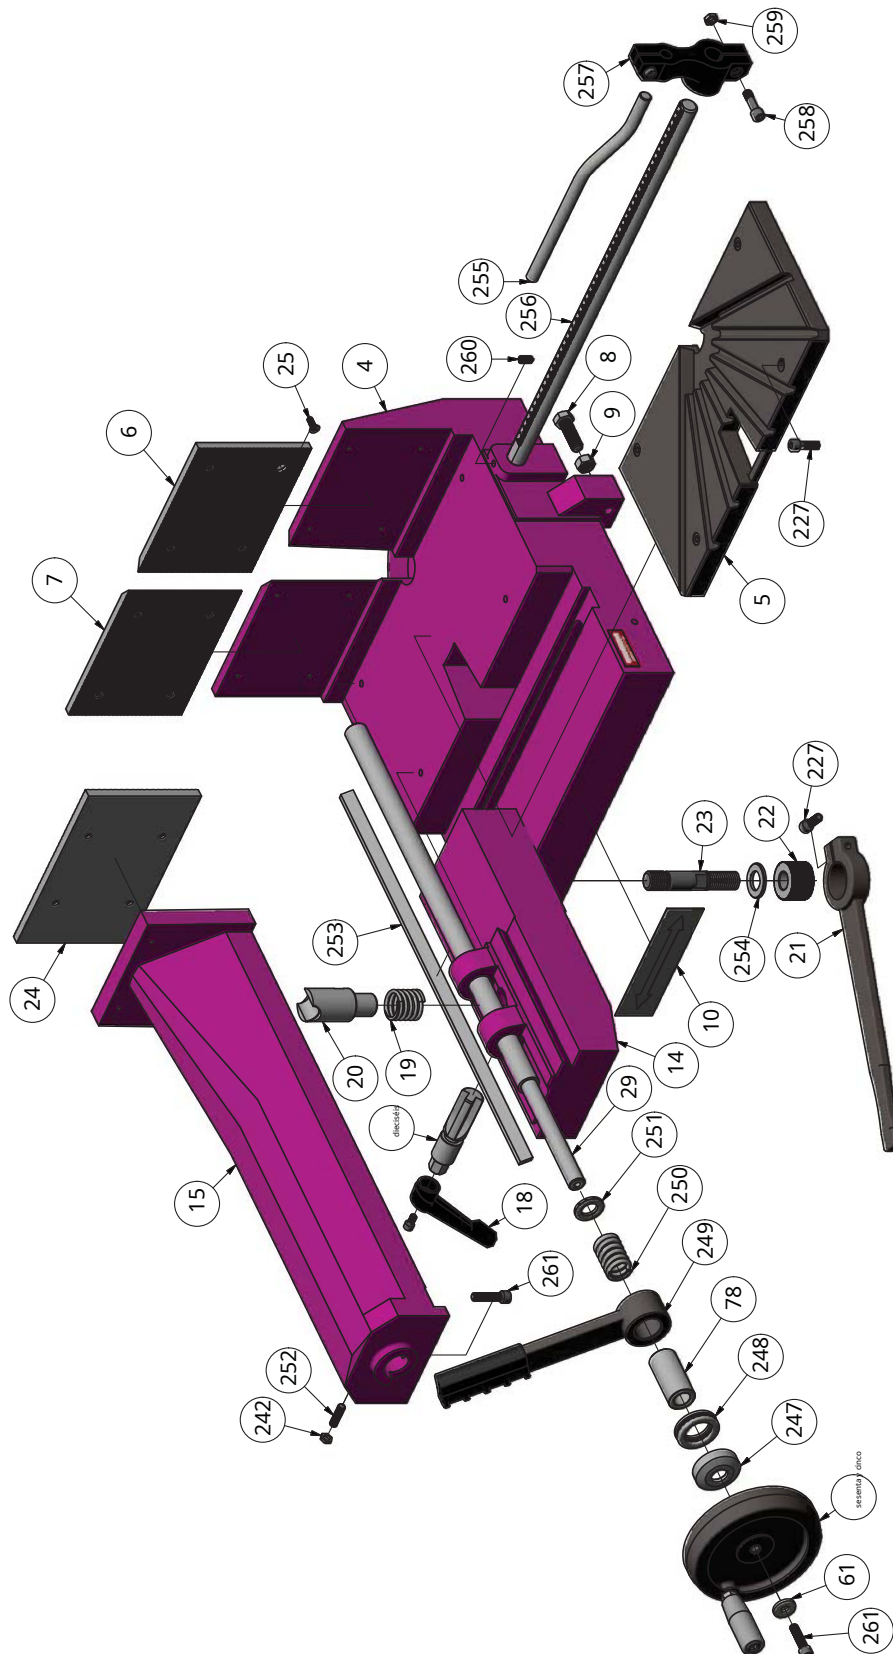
Explosionszeichnung - Dibujo de piezas de repuesto
